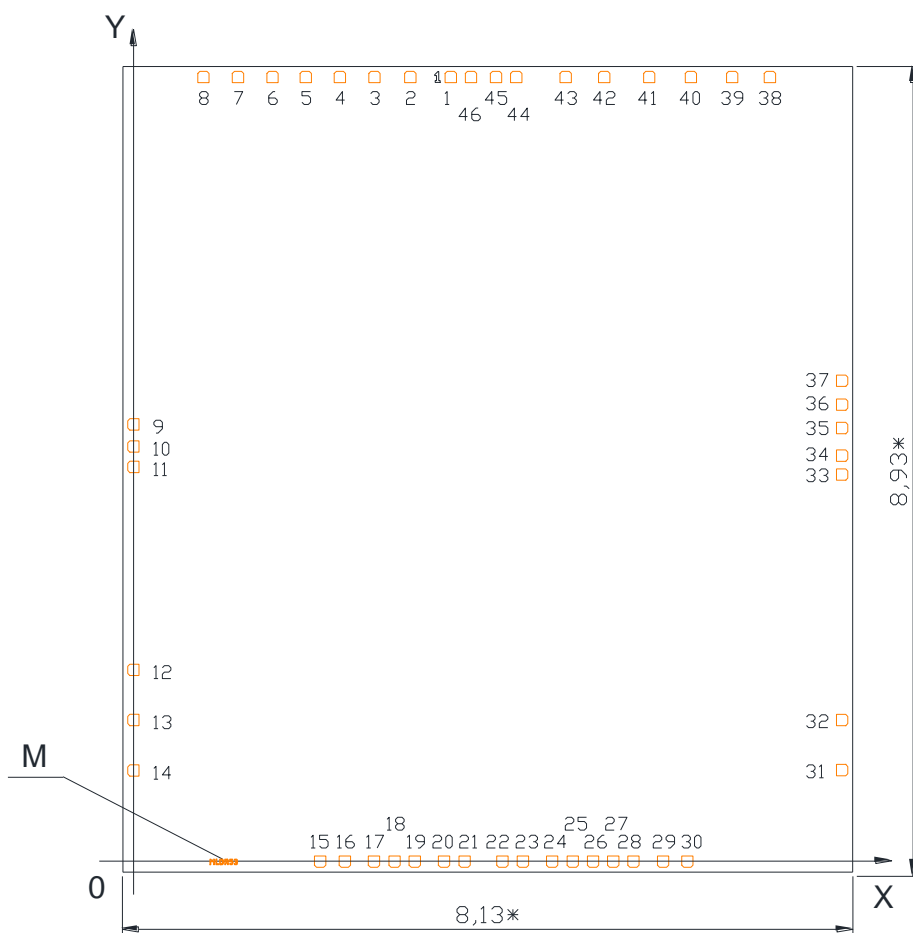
Габаритный чертеж корпуса 5134.64-6
